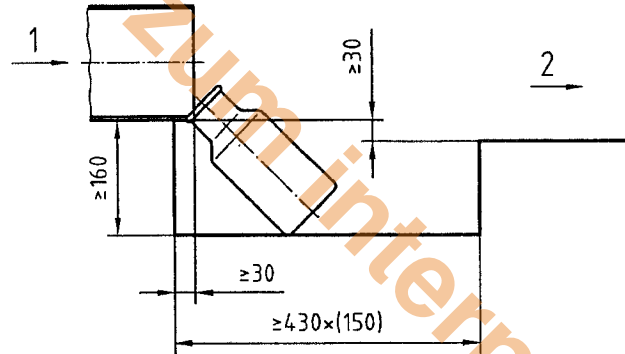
Mindestmaße der Probenahmeeinrichtung
